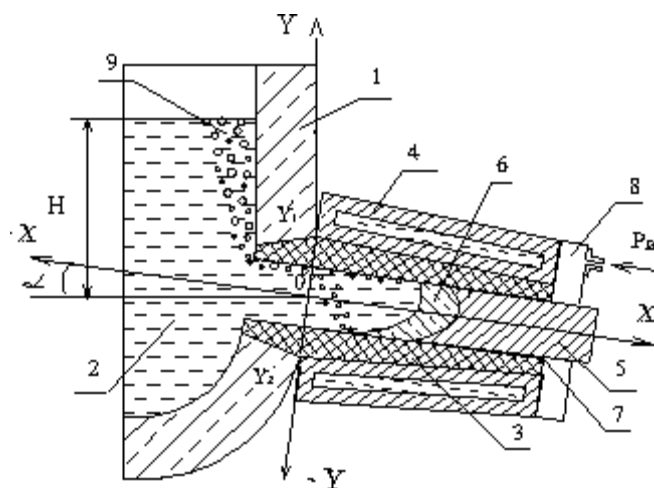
Схема пропускания газовой смеси в зазоре между поверхностями заготовки и графитовой втулки кристаллизатора:
